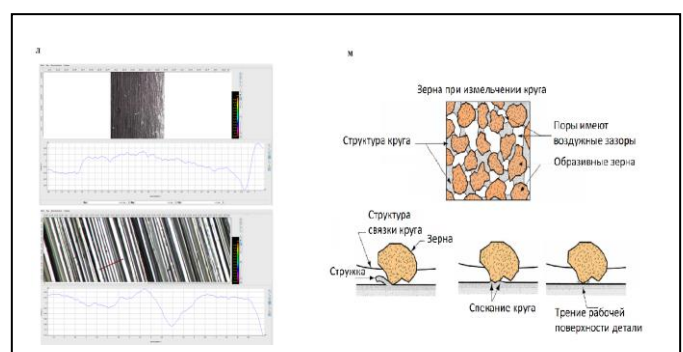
Сколы (k) при полировке зубчатых колес для выявления шероховатости поверхности зубчатой части (m)
